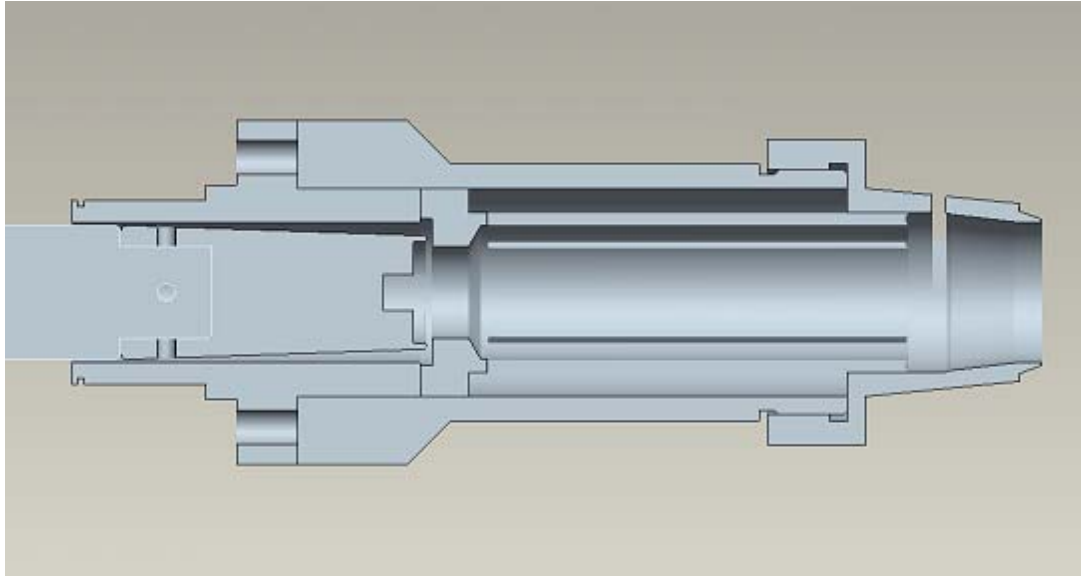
Tredimensionell CAD-bild av monteringsmekanism.
